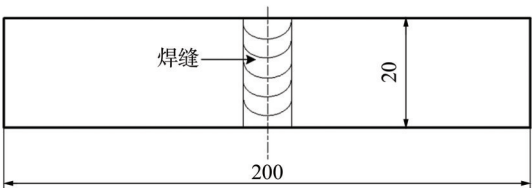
焊接接头弯曲试样尺寸(单位:mm)
